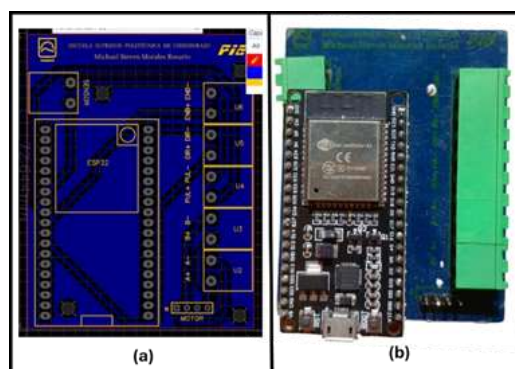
a) Diseño de la placa PCB. b) Placa PCB física
